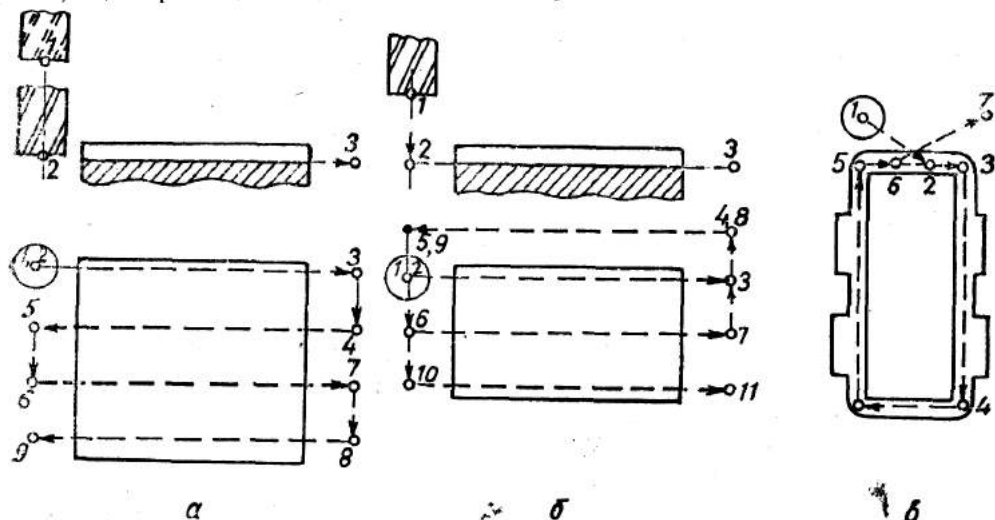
Схеми чорнового (а), чистового (б) і контурного (в) фрезерування площини торцевою фрезою.
